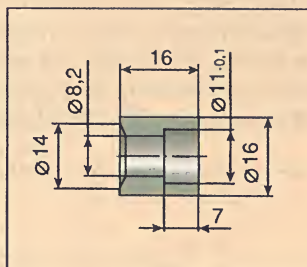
Оправка для запрессовки направляющих втулок клапанов ВАЗ.
